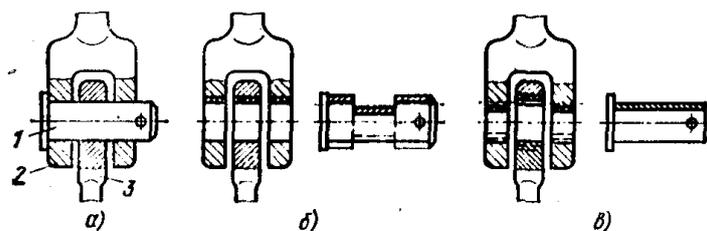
Шарнирное соединение вилки с тягой (форма валика и расположение нолей допусков для наглядности показаны утрированно)
